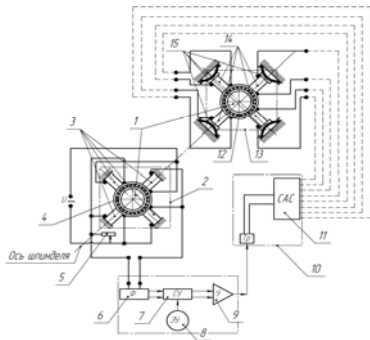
Устройство для гашения колебаний шпинделя металлорежущего станка
